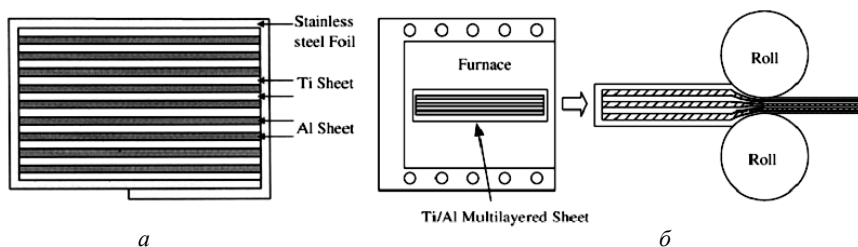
Схема процесса получения металло-интерметаллидного слоистого композита; *а* – многослойная заготовка; *б* – горячая прокатка [32, 33]
